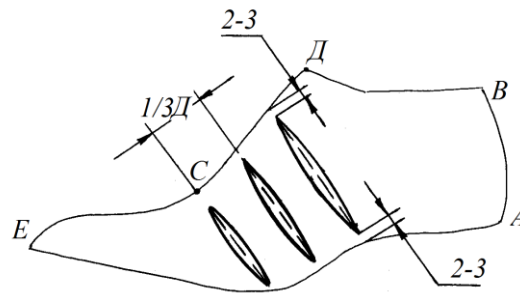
Розтин зліпка зовнішньої бічної поверхні колодки
